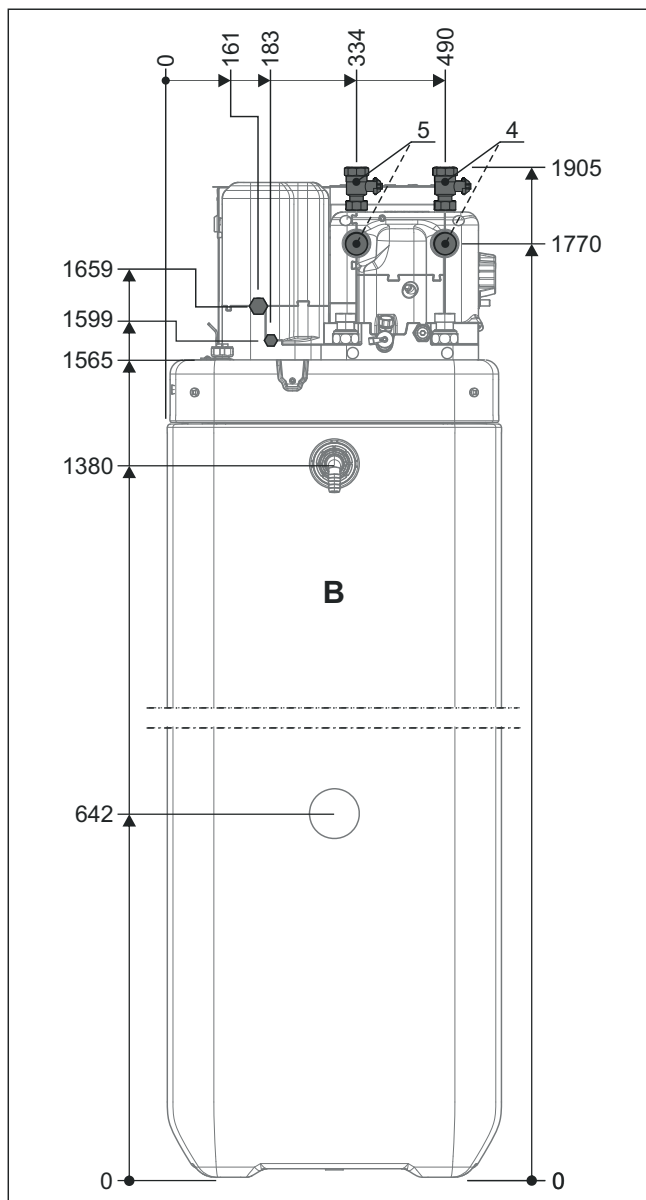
Dimensioni vista laterale - ...04P30D/...08P30D
